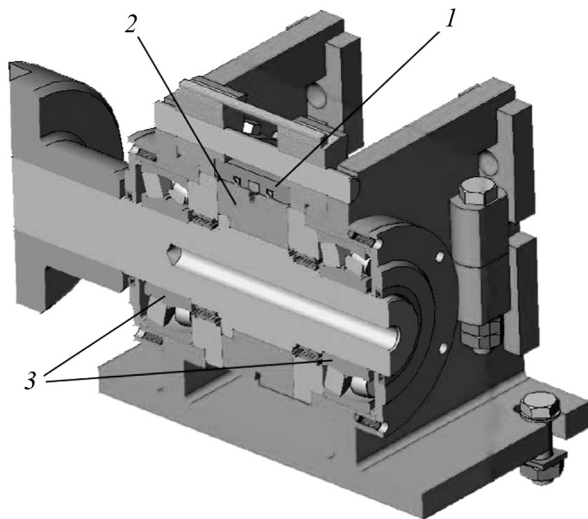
Прессовый узел установки Conform (разрез) с новой системой крепления башмака
